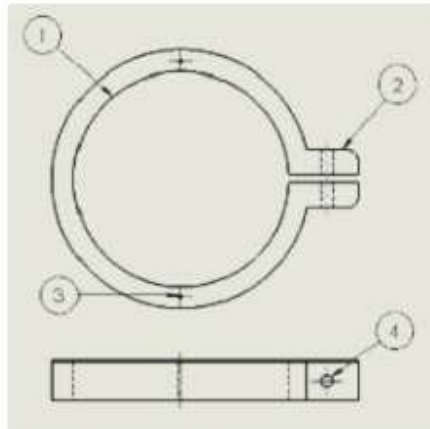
Variables de diseño del anillo sujetador del embudo. Fuente: Autor.
